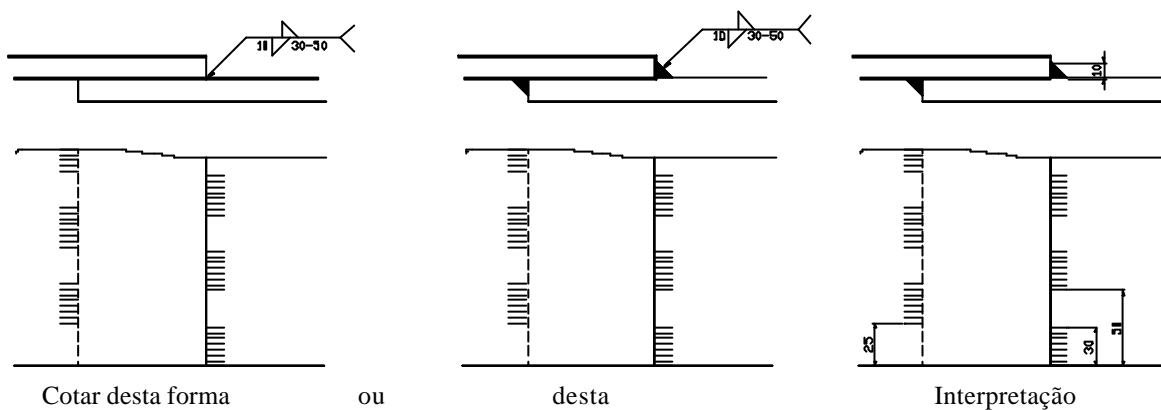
Cotagem com comprimento e passo defasado do cordão de solda
